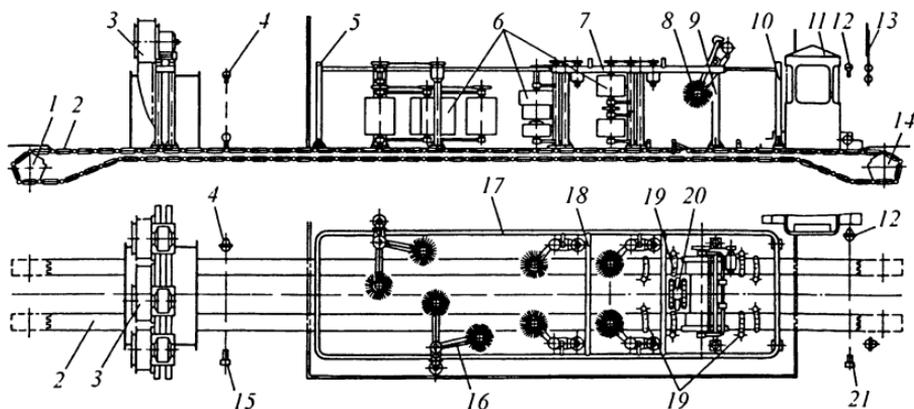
Щеточная моечная установка с автоматическим управлением: 1 — звездочка приводной станции; 2 — тяговая цепь; 3 — вентиляторы; 4, 12 — фотоэлементы; 5, 10 — душевые рамки; 6, 8 — щетки; 7 — стойка; 9 — портал; 11 — кабина оператора; 13 — светофор; 14 — звездочка натяжной станции; 15, 21 — прожекторы; 16 — спаренные распашные щетки; 17, 18 — трубы; 19, 20 — устройства обмыва днища
